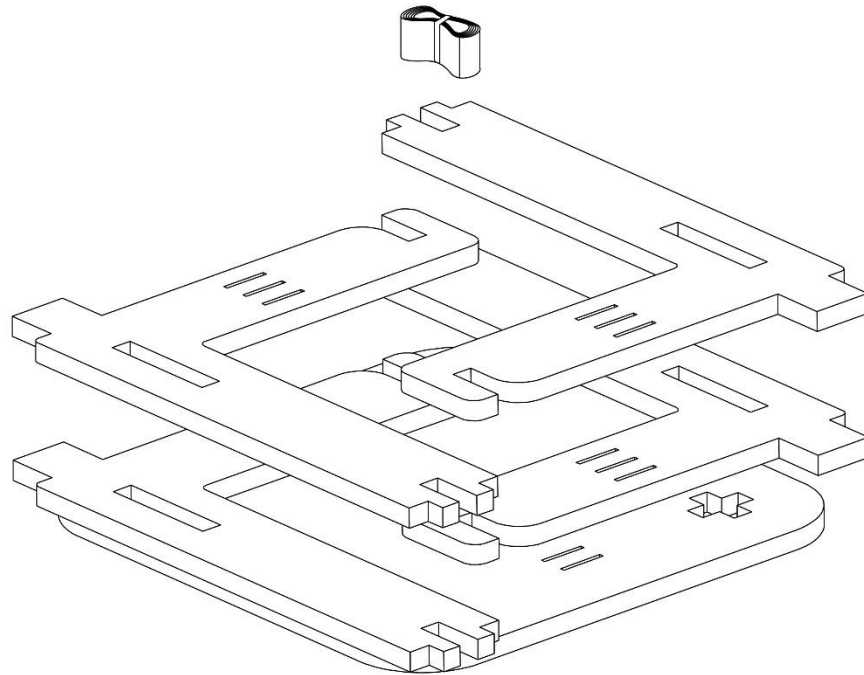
1 Vista explosionada de los componentes en posición de embalar
